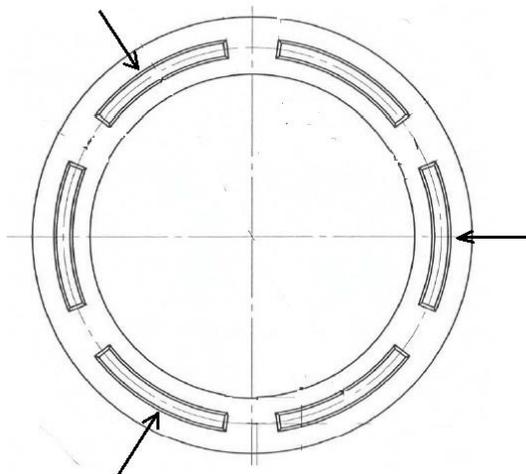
Вид снизу на корпус люка типа ППЛ:
